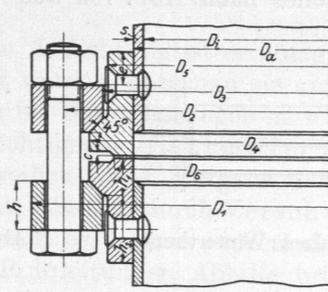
Flanschverbindung mit eingewalztem Rohr.
